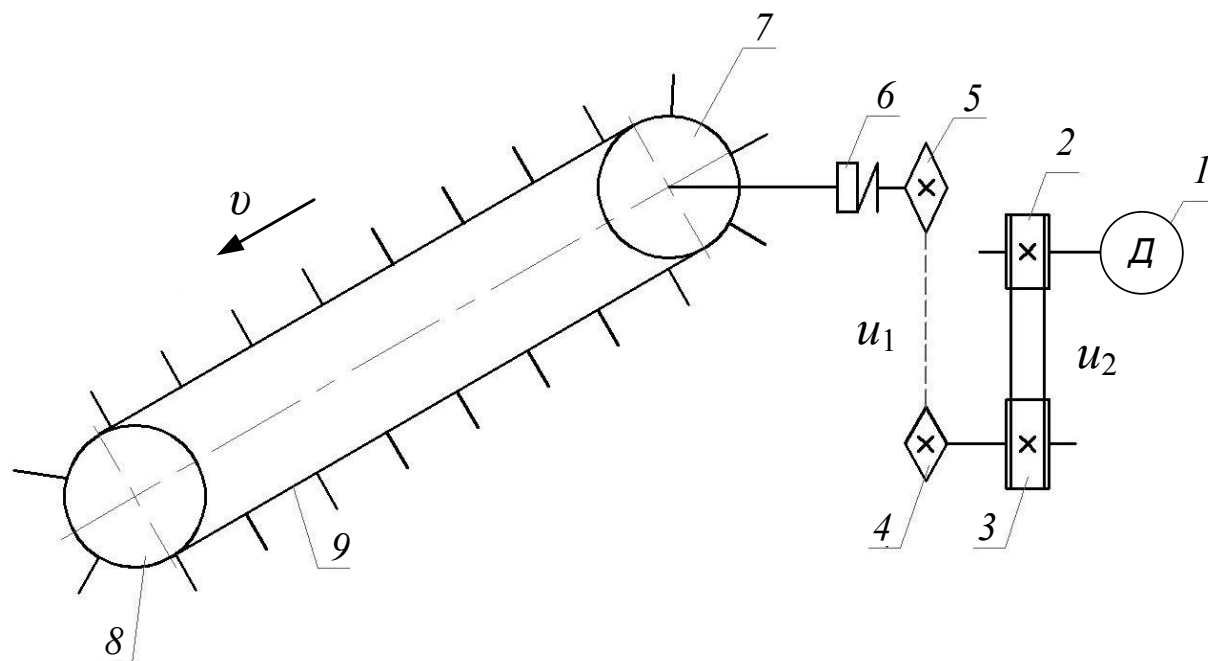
Кінематична схема скребкового конвеєра: 1 – двигун; 2, 3 – шків пасової передачі; 4, 5 – зірочки ланцюгової передачі; 6 – муфта; 7 – привідна зірочка; 8 – привідна зірочка скребкового конвеєра; 9 – ланцюг зі скребками
